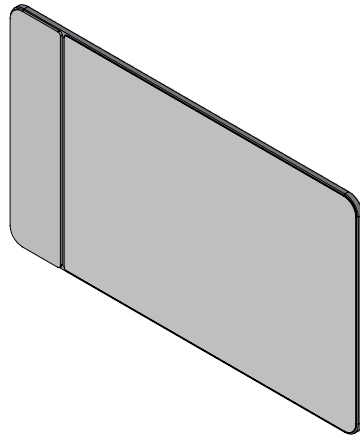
Fig. A Instructions d'installation Tableau be! Wall avec attaches en verre et en PET ainsi que son système de fixation TruMount™
